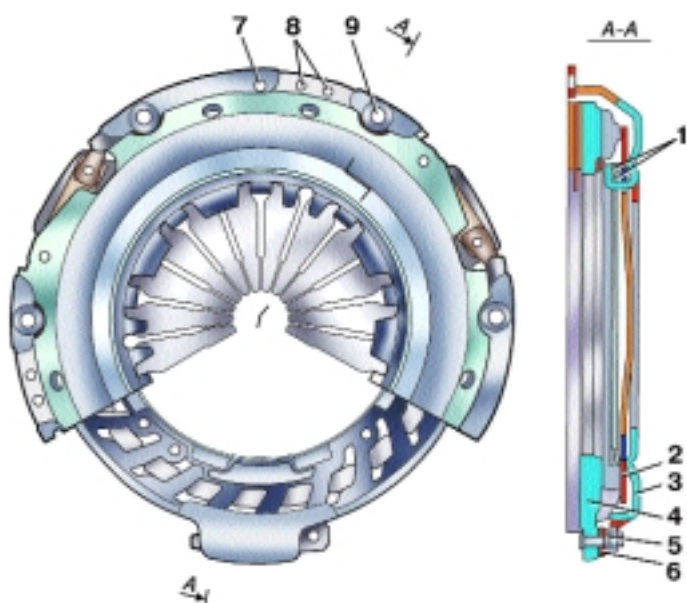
Нажимной диск сцепления «Валео» с кожухом в сборе: 1 – опорные кольца; 2 – диафрагменная пружина; 3 – кожух сцепления; 4 – нажимной диск; 5 – заклепка; 6 – соединительная пластина; 7 – отверстия под установочные штифты; 8 – балансирующие грузики; 9 – крепежные отверстия
